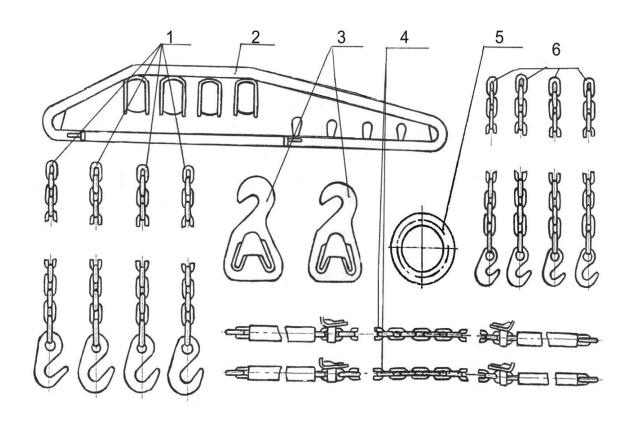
Комплект захватов для агрегатов 1 и 6 – стропы; 2 – траверса; 3 – серьга; 4 – цепь; 5 – кольцо.
